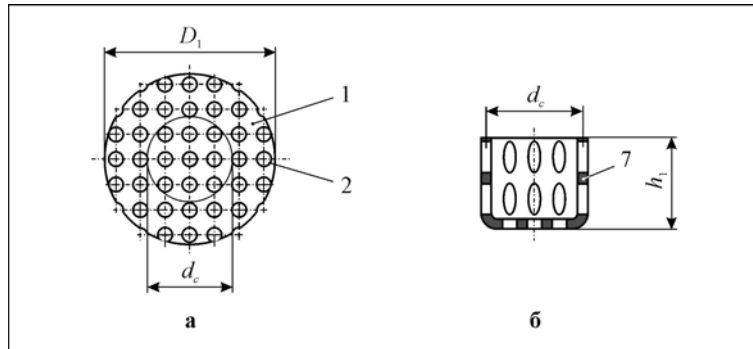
Заготовка (а) та деталь (б) після витягування за пунктом 1
